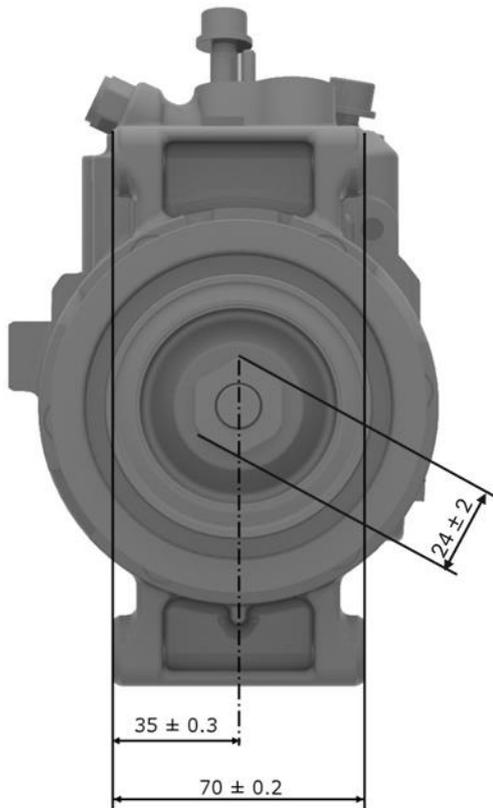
Dimensions du compresseur de fluide frigorigène, vue de face (exemple DENSO-7SEU17)
